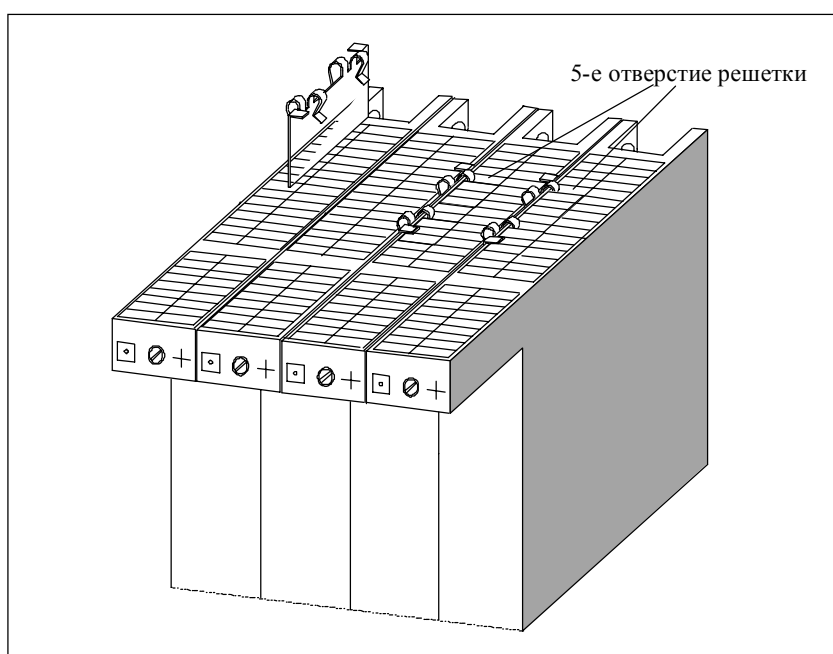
Крепление модулей соединительными зажимами (схема)
